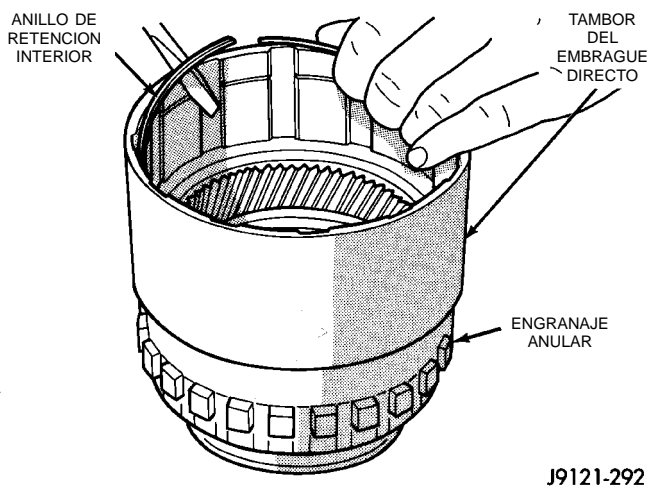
Desmontaje del anillo de retención interior del tambor de embrague
